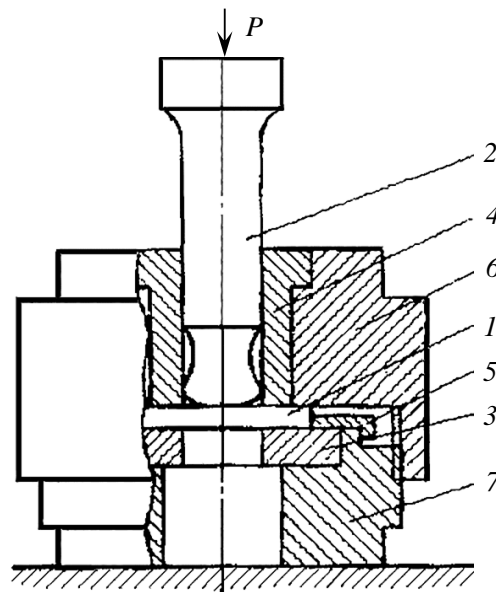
Схема приспособления для испытания на срез листа по круговому контуру: 1 – образец; 2 – пуансон; 3 – матрица; 4 – направляющая втулка; 5 – фиксирующее кольцо; 6 – прижимная гайка; 7 – основание [3]
